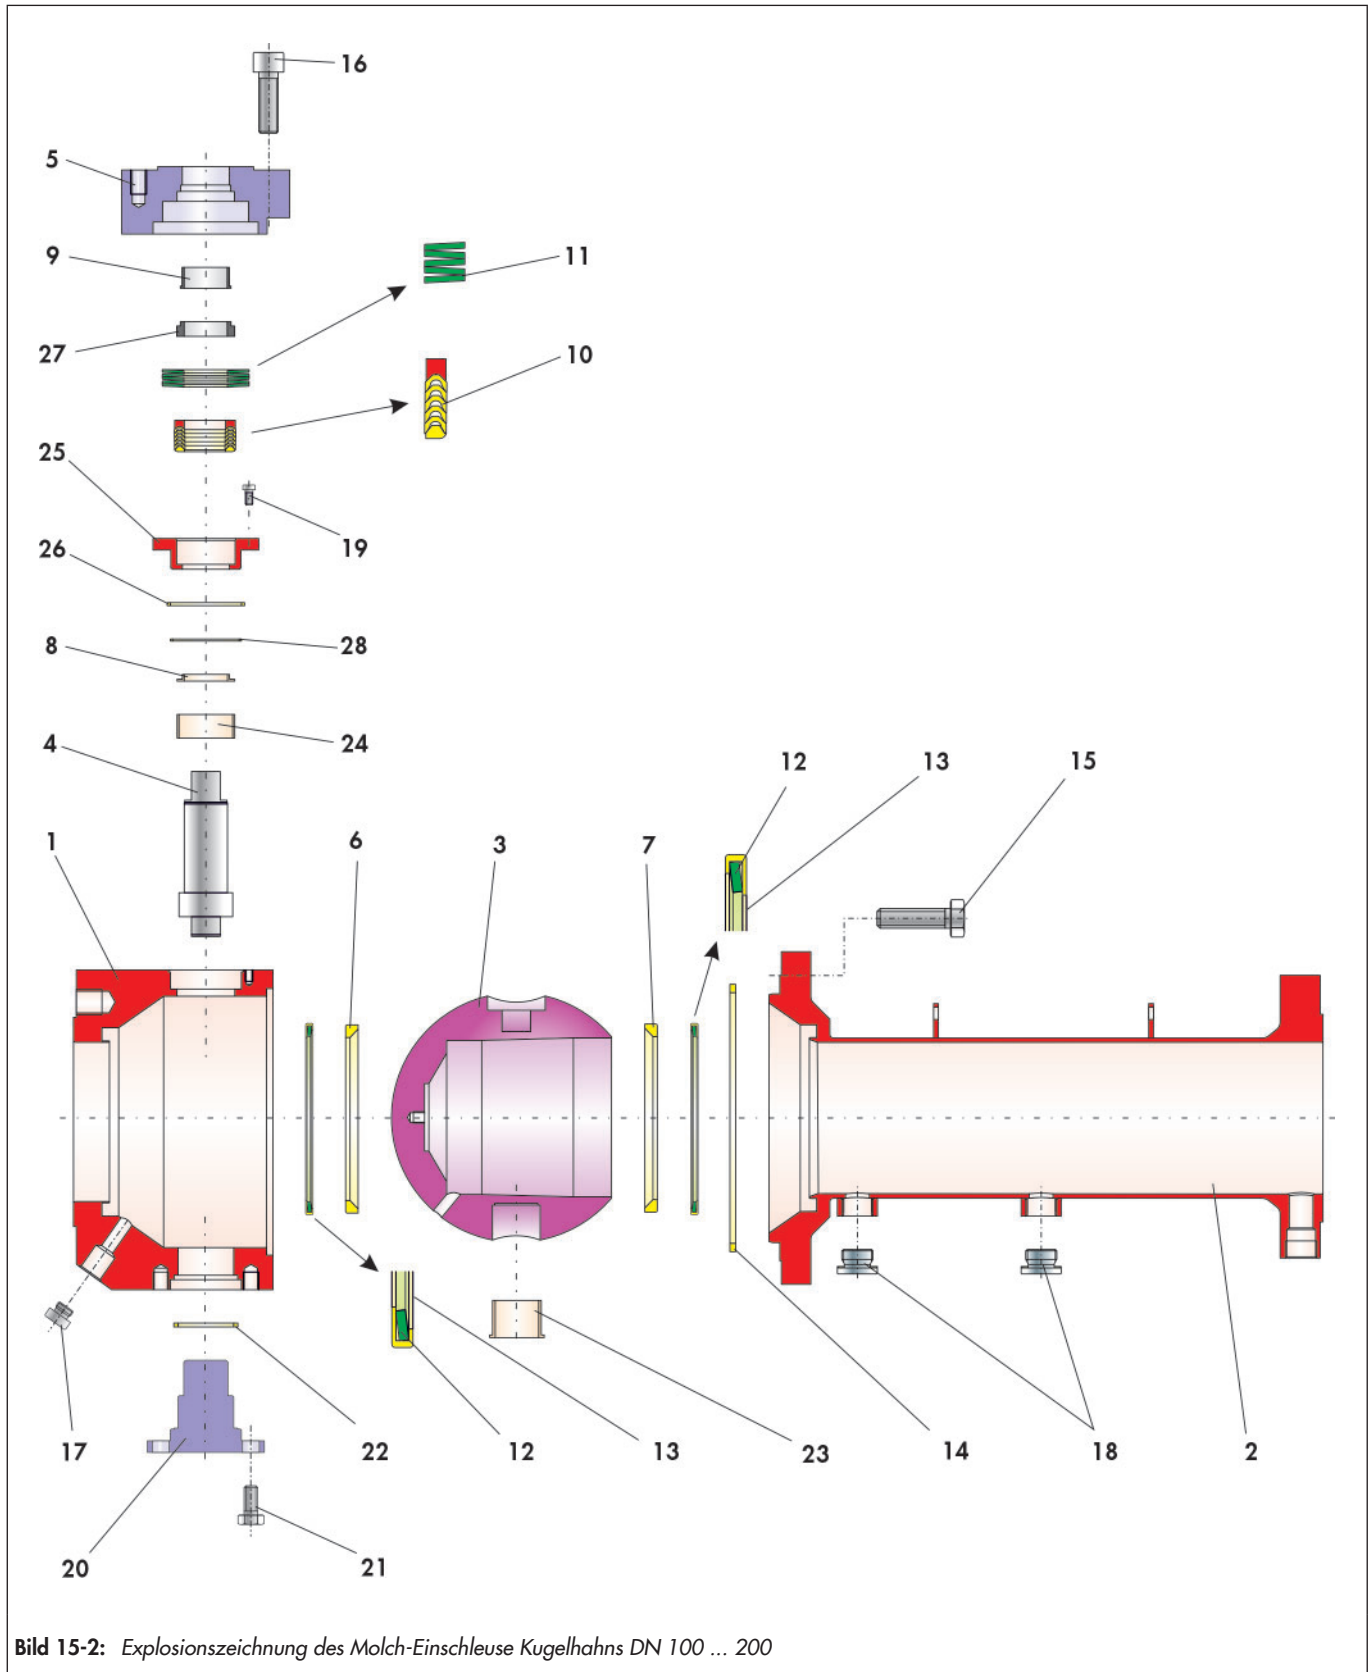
Explosionszeichnung des Molch-Einschleuse Kugelhahns DN 100 ... 200
